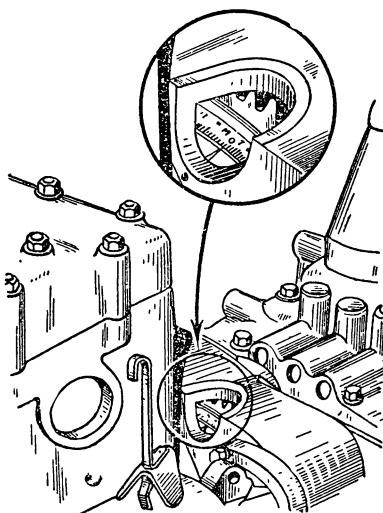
Установка поршня первого цилиндра в крайнее верхнее положение по указателю в лючке картера сцепления и шарика маховика
